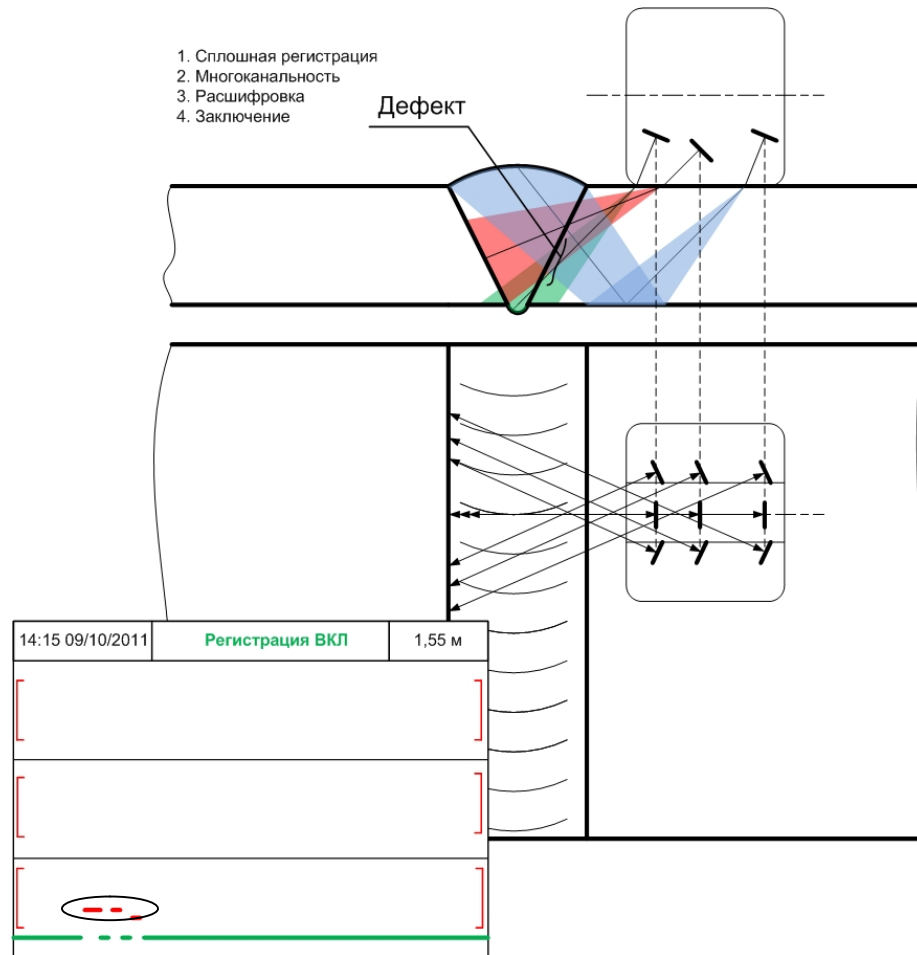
Пример реализации многоканального колесного преобразователя для контроля сварных соединений
